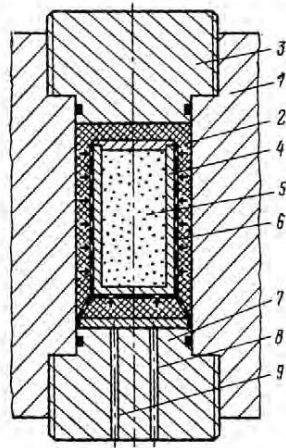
Основная схема изостатического прессования: 01 - сосуд высокого давления; 2 - жидкость под высоким давлением; 3-верхний затвор; 4 - эластичная форма; 5-прессовый порошок; 6 - перфорированная корзина; 7-нижние ворота; 8 - высокое давление; 9 - сточные воды
